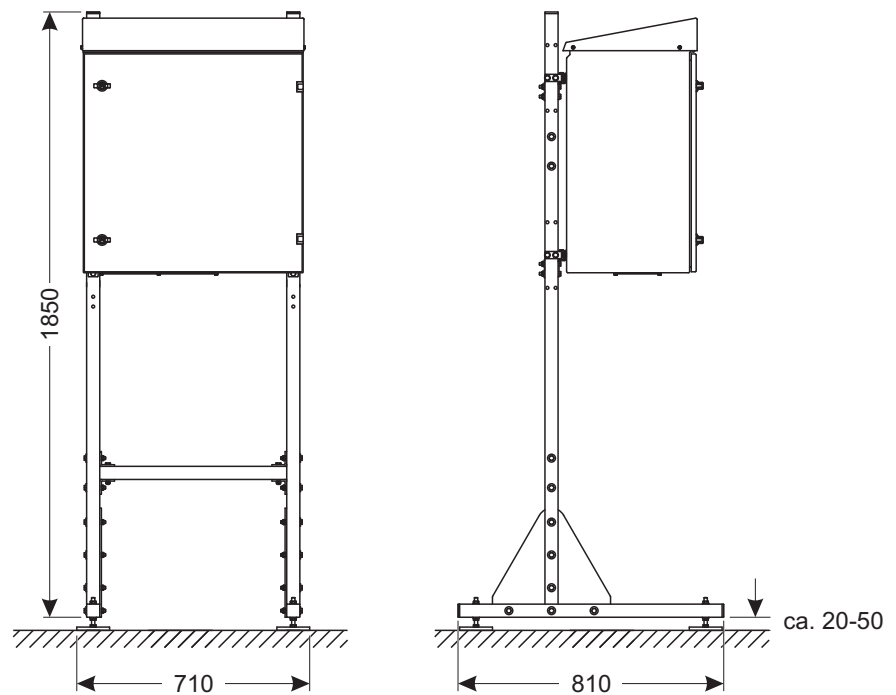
Maßzeichnung P 700 IQ Montage an einer Standsäule (Maße in mm)
